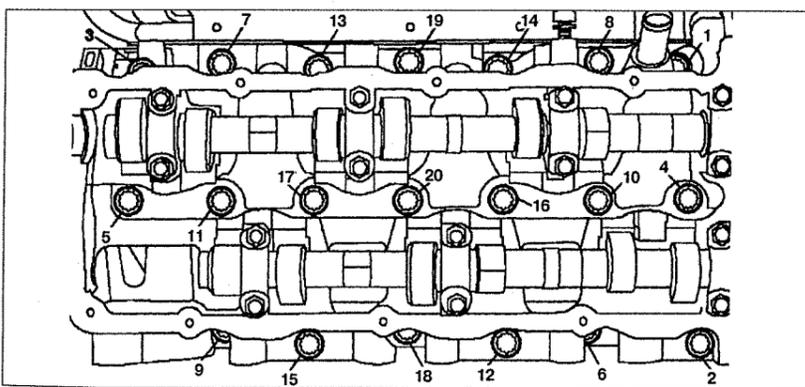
Порядок ослабления болтов головки блока цилиндров.
